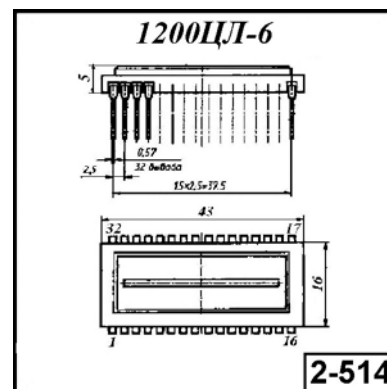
Внешний вид и габаритные размеры 1200ЦЛ6
